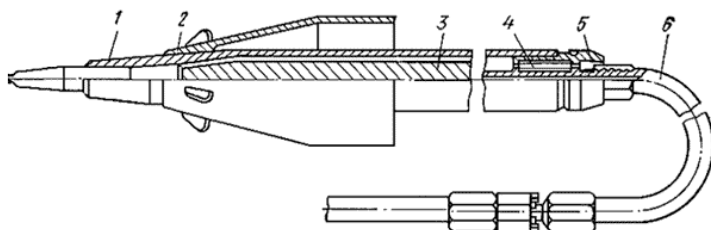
Пневмопробойник: 1 - корпус; 2 - съемный расширитель; 3 - ударник; 4 - золотник; 5 - реверсивное устройство; 6 - рукав.
